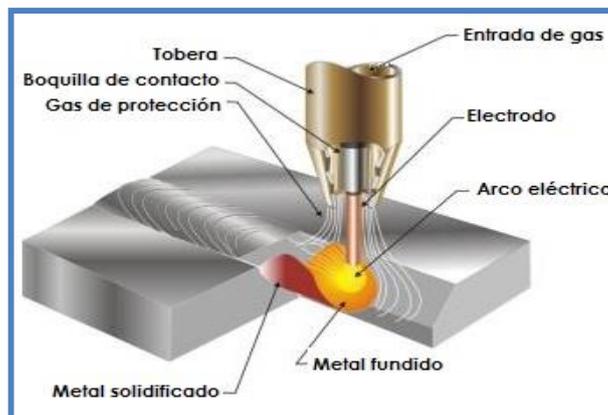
ESQUEMA DE LA SOLDADURA GMAW
